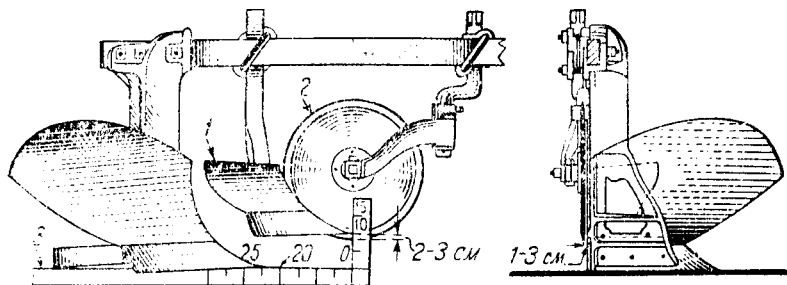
Установка предплужника и дискового ножа у плугов с плоской рамой:
